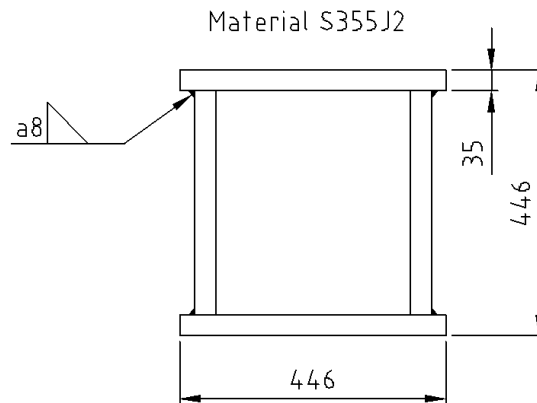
Tubo armado formado por soldaduras en ángulo
